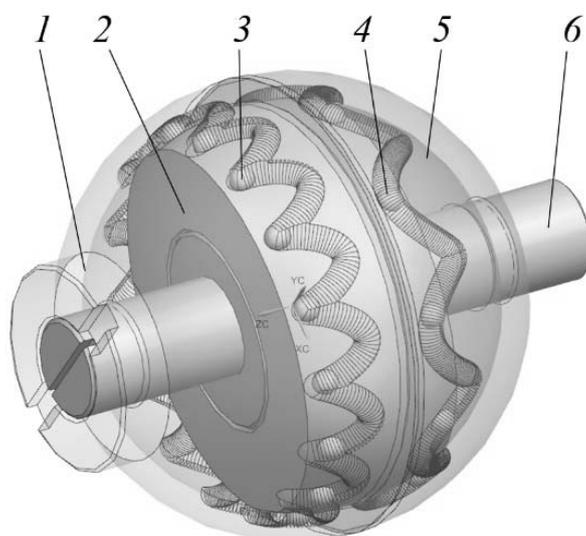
Компьютерная модель СШП: 1 – входной вал; 2 – сателлит; 3, 4 – шарики; 5 – корпус; 6 – выходной вал
